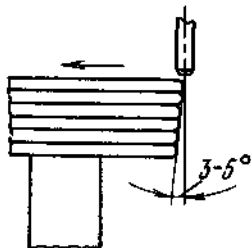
Сборка листов в пакет, облегчающая начало процесса резки
